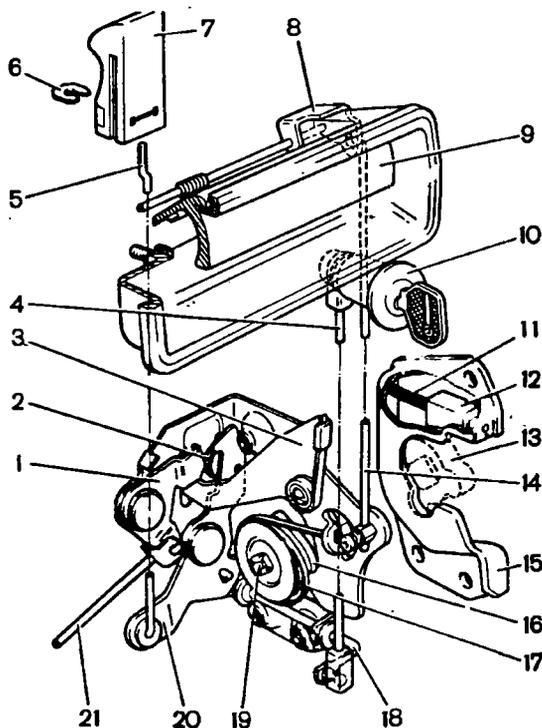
Замок передней левой двери: 1 - рычаг внутреннего привода замка; 2 - пружина рычага блокировки замка; 3 - рычаг наружного привода; 4 - тяга выключателя замка; 5 - тяга кнопки блокировки замка; 6 - скоба; 7 - кнопка блокировки замка; 8 - поводок тяги наружного привода; 9 - наружная ручка замка; 10 - выключатель замка; 11 - пружина сухаря; 12 - сухарь фиксатора; 13 - ротор замка; 14 - тяга наружного привода; 15 - корпус фиксатора замка; 16 - храповик замка; 17 - пружина центрального валика; 18 - валик выключения замка; 19 - центральный валик; 20 - рычаг блокировки замка; 21 - тяга внутреннего привода замка
